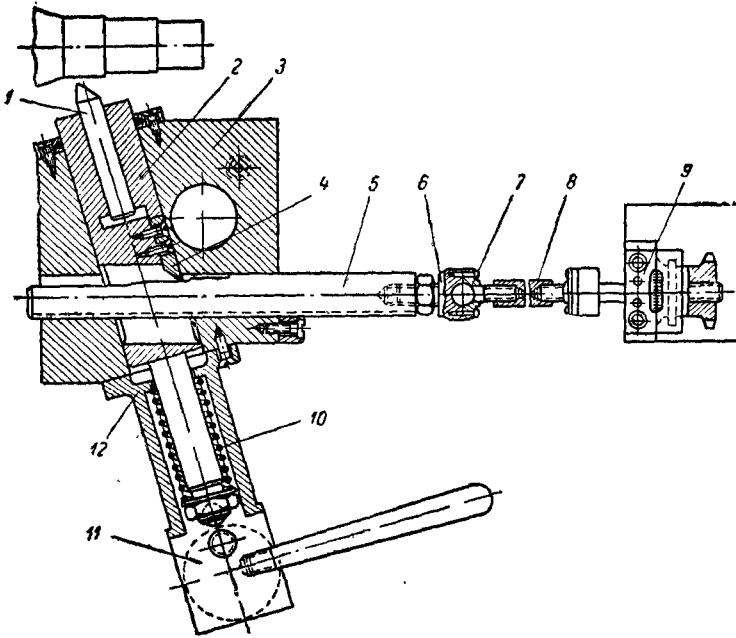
Копировальное приспособление для обработки ступенчатых валов конструкции В. К. Семинского.
